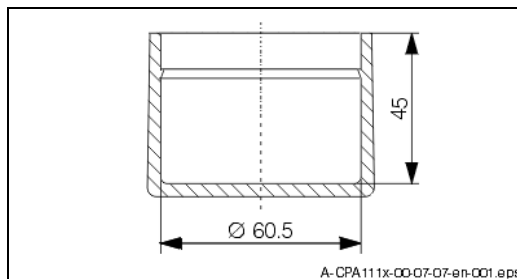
Dimensiones del capuchón de calibración volumen máx. de llenado 70 ml
